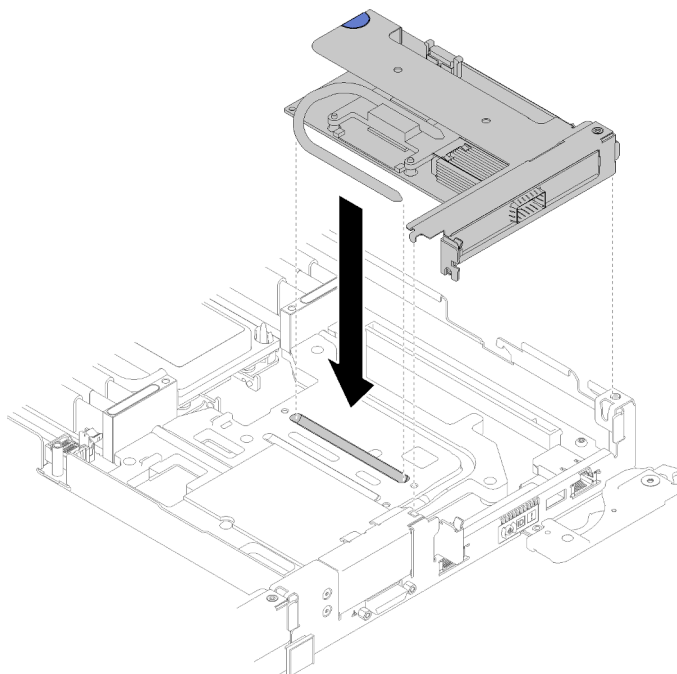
Instalação do conjunto de gaiola de placa riser PCIe
